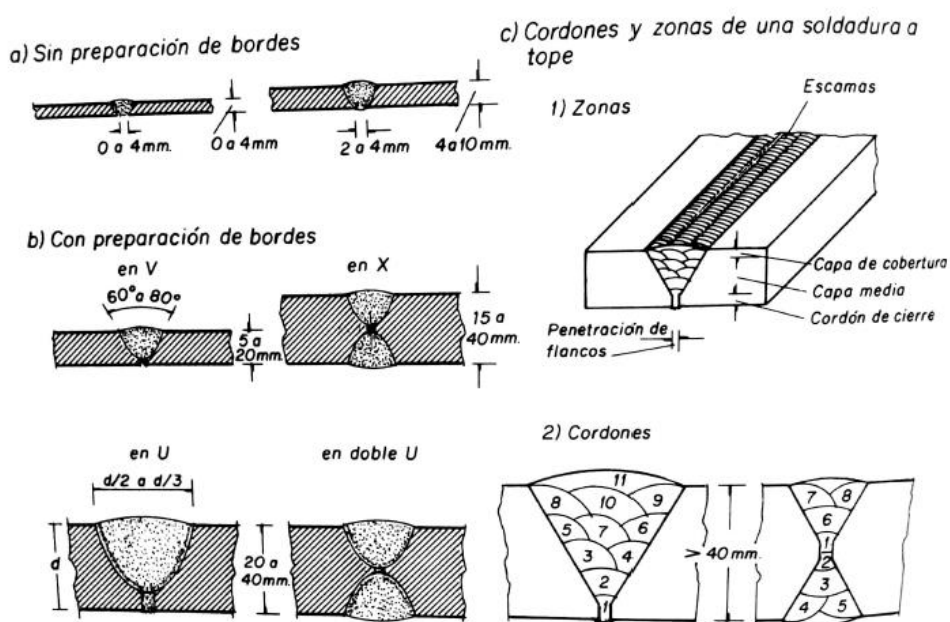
Soldaduras a tope de penetración completa de chapas situadas en un mismo plano.
